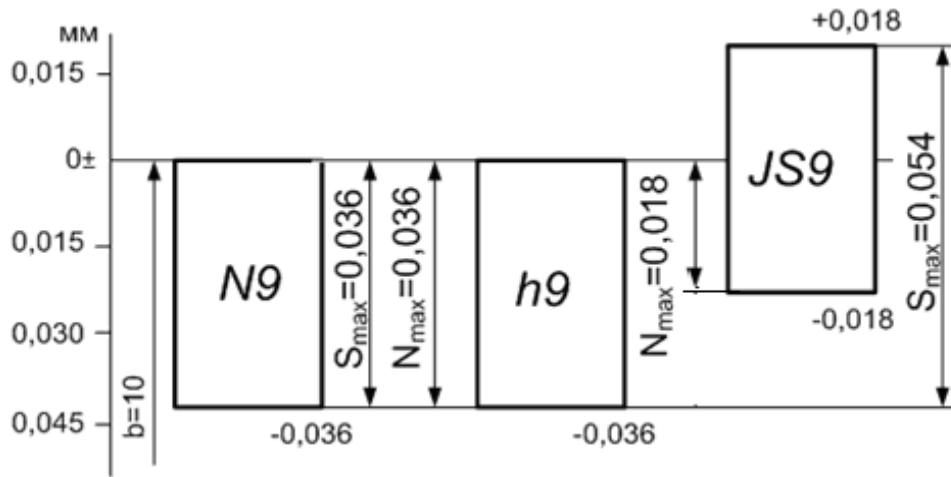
Схема полів допусків шпонкового з'єднання 7.Складальний і подетальні кресленики шпонкового з'єднання. Складальний і подетальні кресленики шпонкового з'єднання наведено на рис. 8.2.
